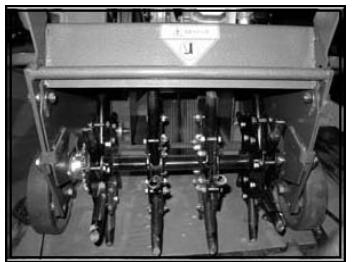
Le rotor chute si les assemblées de roulement sont retirées
